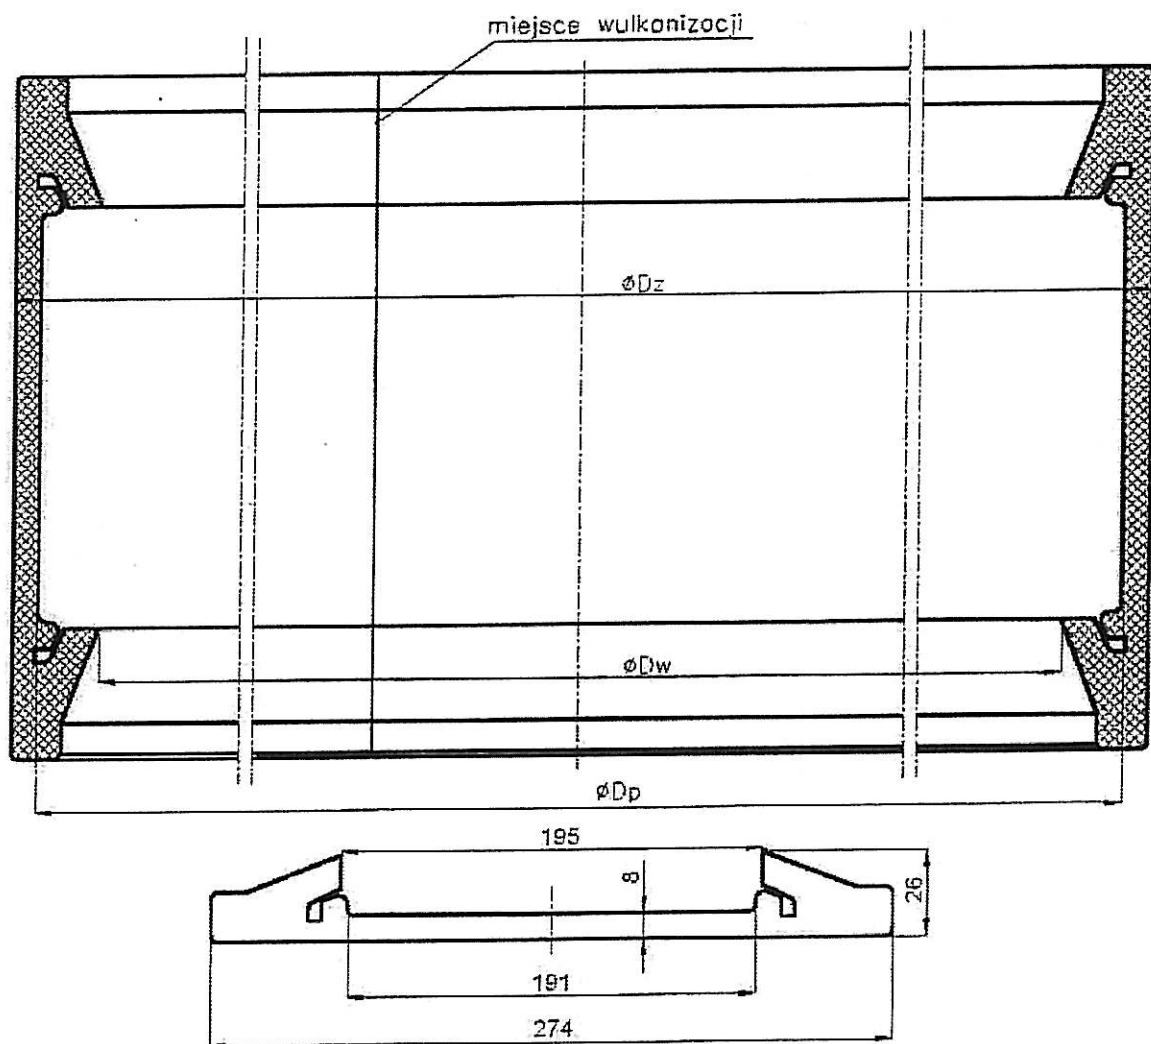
Parametry techniczne i warunki montażu łącznika PF-S/S
